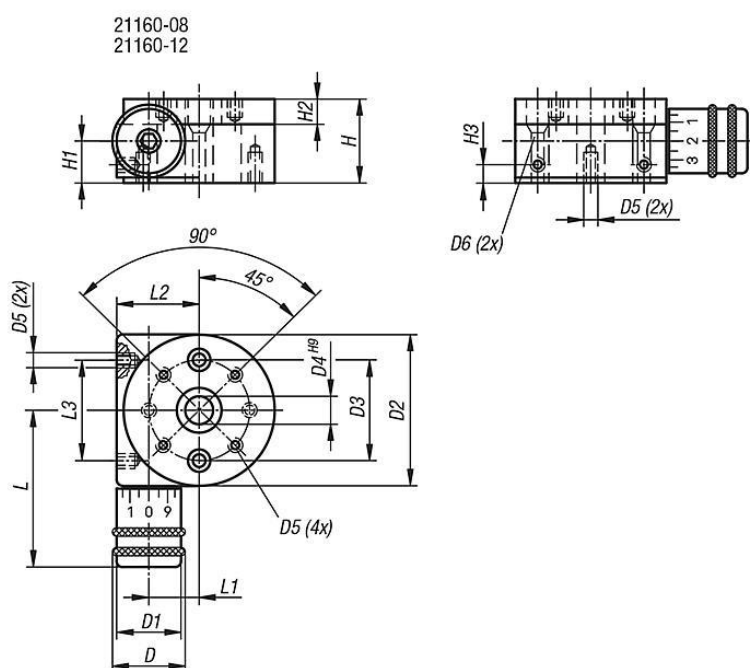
Чертёж габаритных размеров поворотного стола «NORELEM»
